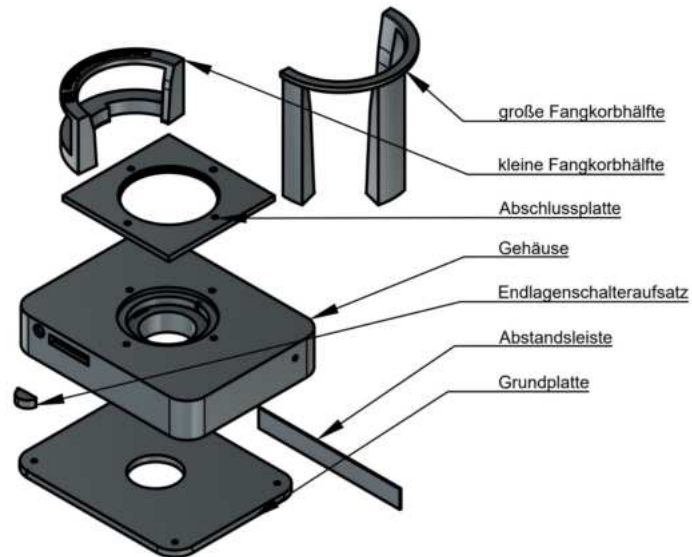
3D-gedruckte Komponenten des Getränkeschlittens
